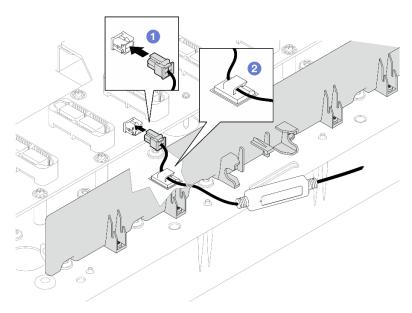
Conexión del cable del sensor de filtraciones a la tarjeta de interposición
